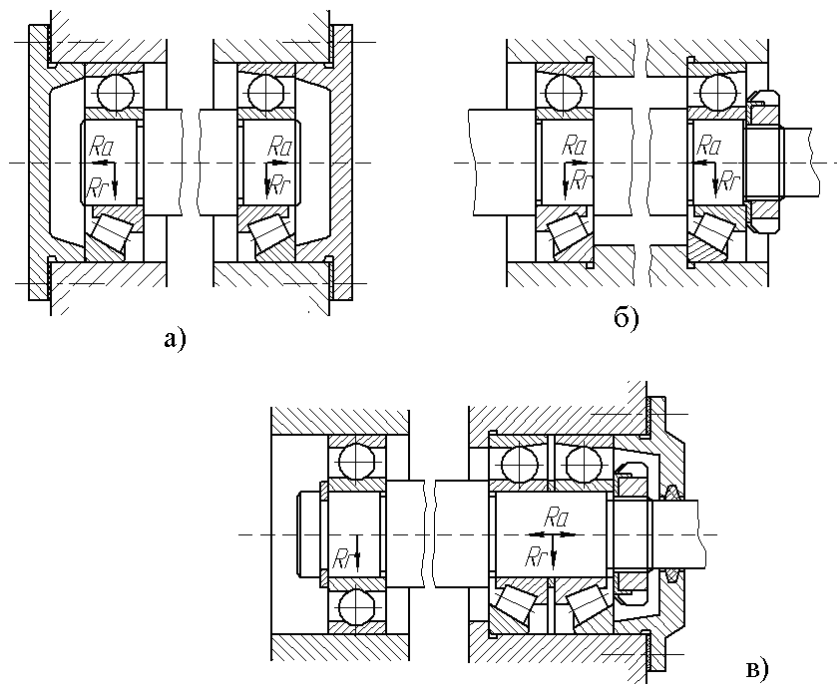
Конструкції опор валів на радіально-упорних підшипниках.
